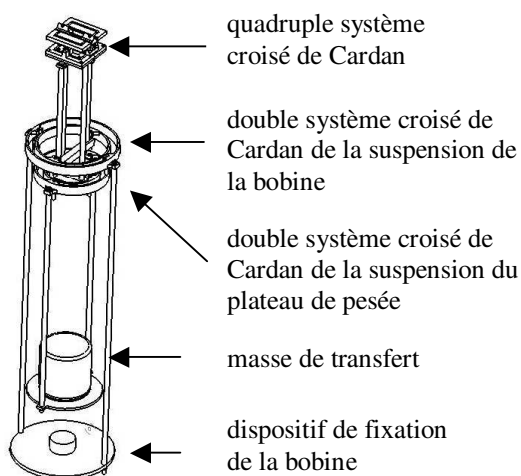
Double ligne de suspension du plateau de pesée et de la bobine.
